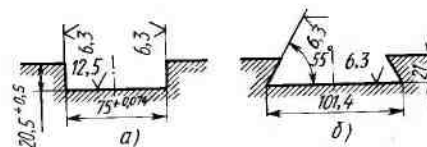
Последовательность обработки паза типа «ласточкин хвост»: а — фрезерование прямоугольного паза, б — фрезерование скосов
